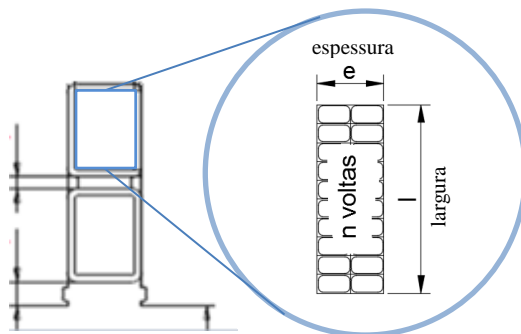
Recorte do plano de bobinagem - Dimensões da bobina no estator
